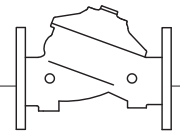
Проверка диафрагмы в линии без демонтажа корпуса
